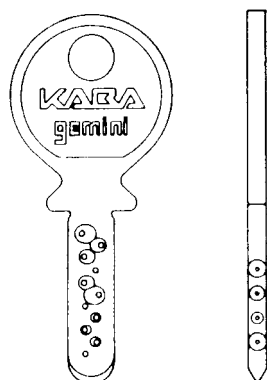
Любая заготовка Gemini подойдет для изготовления ключа к замку Gemini
